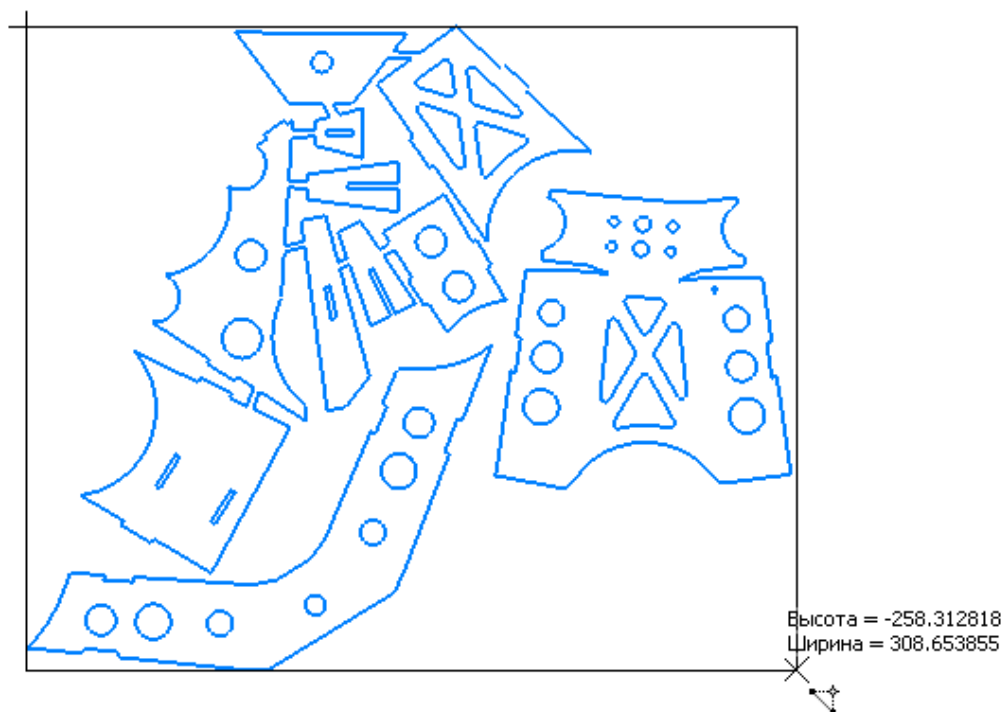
Эскиз деталей для изготовления деталей стального кулака на лазерном станке
